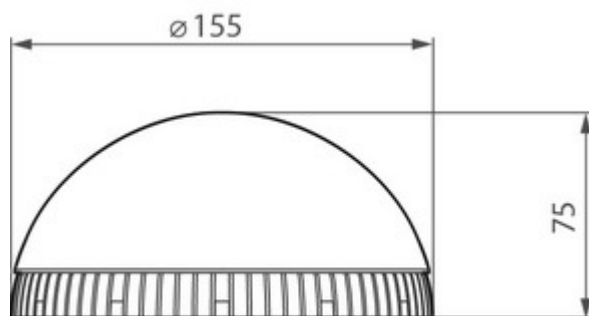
Внешний вид и габаритные размеры светильников.
